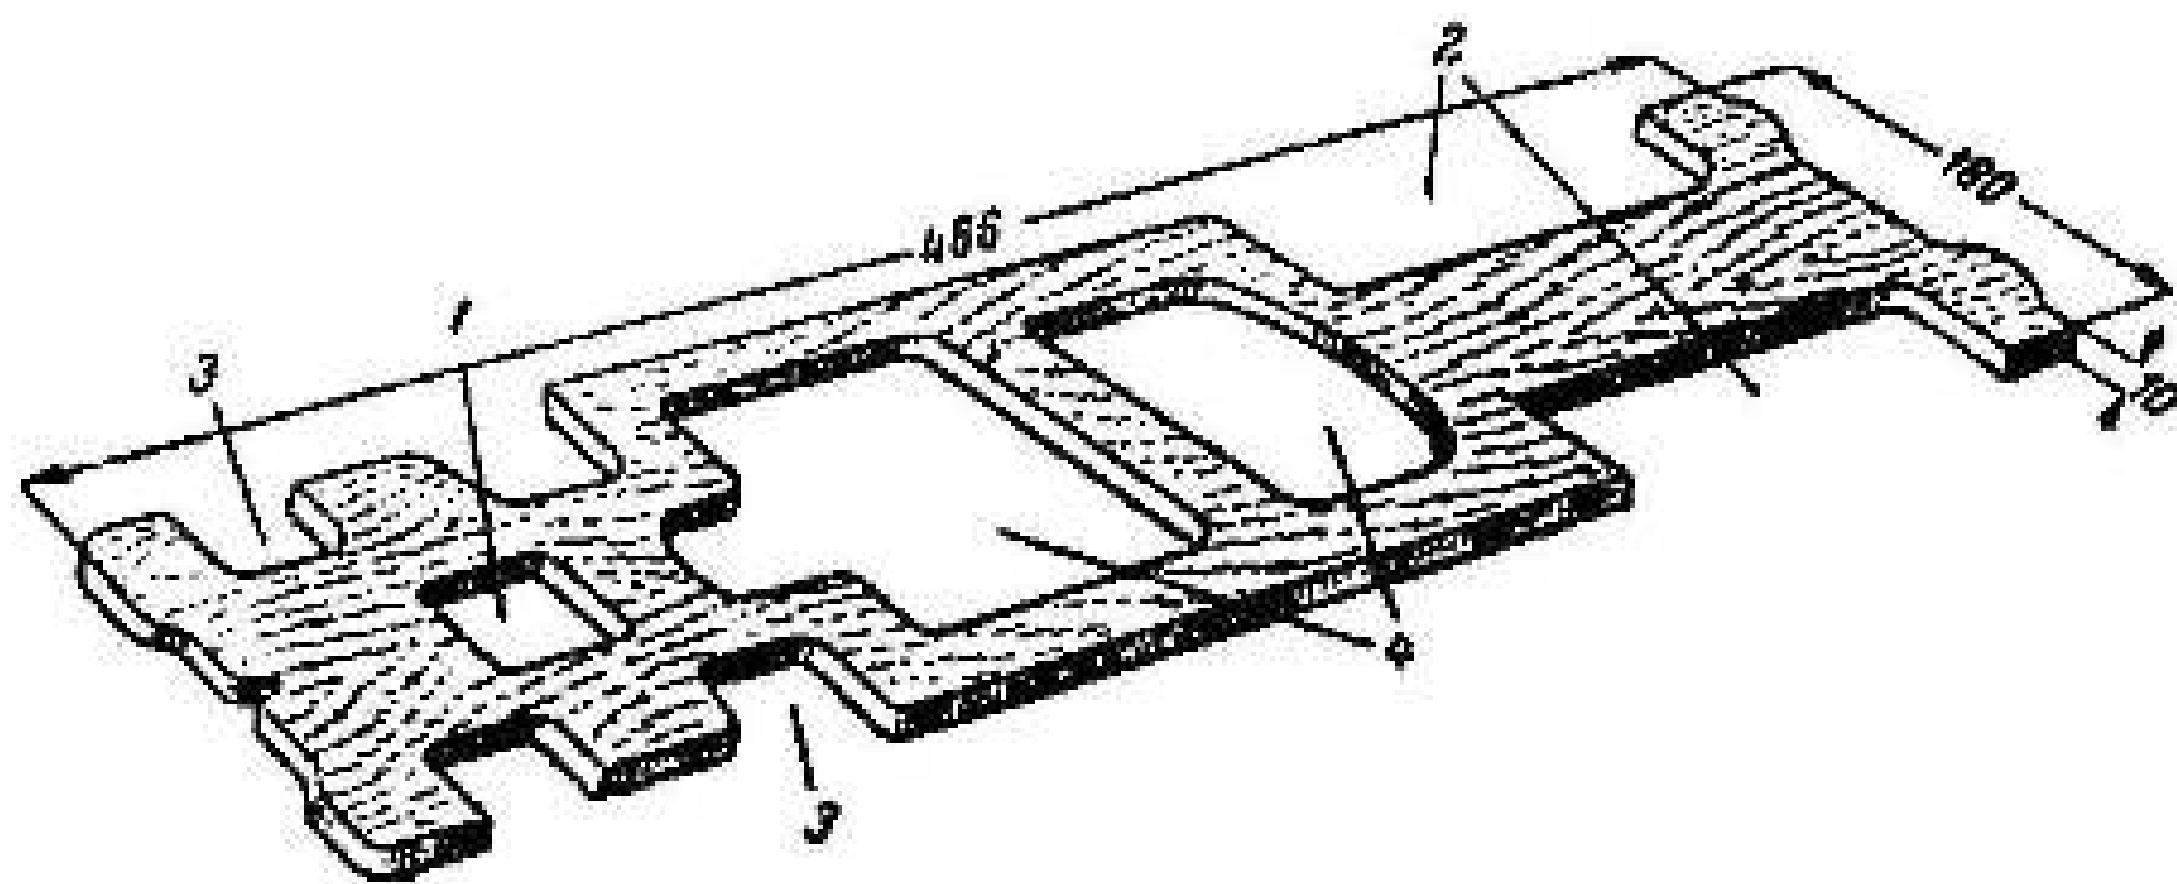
Рама-платформа, изготовленная из десятимиллиметровой фанеры:
